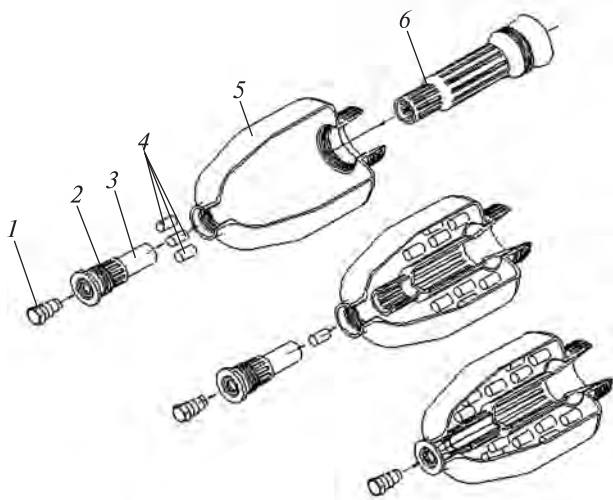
Схема сборки импульсных твердотопливных ракетных двигателей: 1 — пиропатрон, 2 — крышка, 3 — воспламенитель, 4 — заряд, 5 — корпус, 6 — трубка-диафрагма
